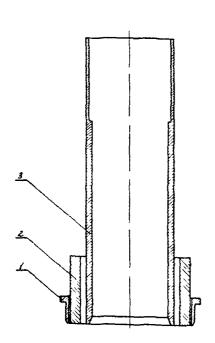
Приспособление для сборки скользящих контактов отделителя:
